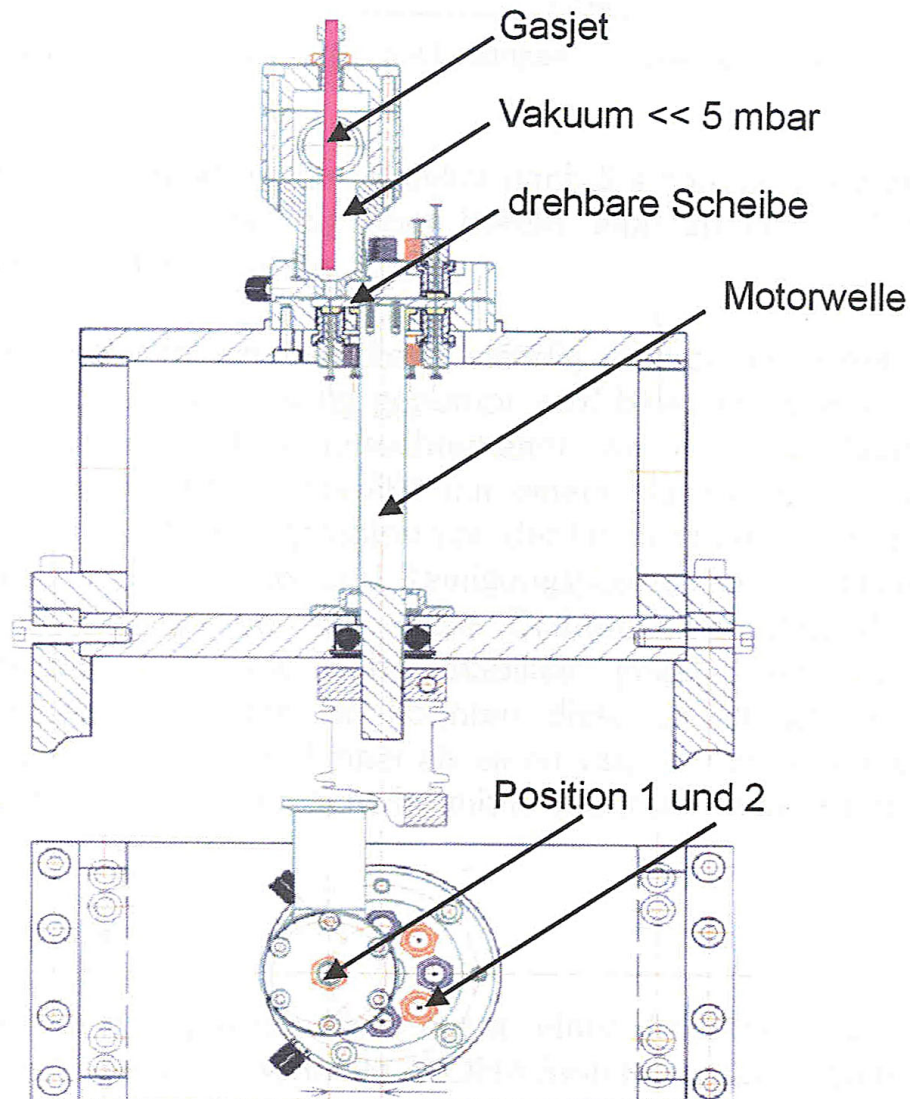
Technische Zeichnung des ALOHA-Systems (oben: Seitenansicht; unten: Draufsicht).
